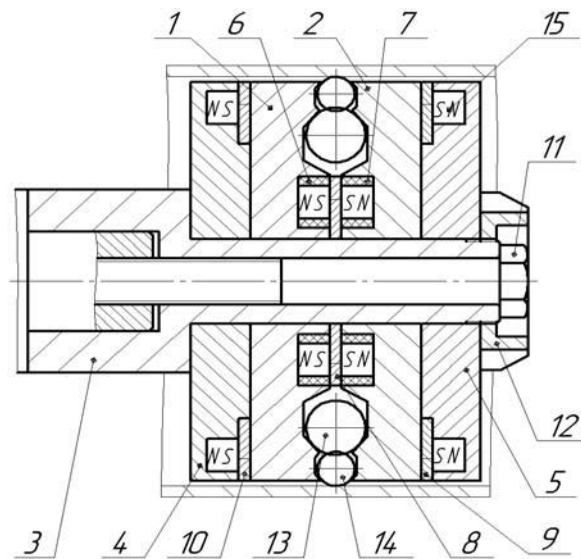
Конструкция магнитно-динамического накатника для модифицирования поверхностного слоя деталей машин и формирования антифрикционных покрытий: 1, 2 – диски; 3 – оправка; 4, 5 – обоймы; 6, 7 – обоймы магнитной системы разгона; 8 – зубчатый магнитопровод магнитной системы разгона; 9, 10 – зубчатые магнитопроводы; 11 – винт; 12 – гайка; 13 – приводные шары; 14 – деформирующие шары; 15 – магниты
